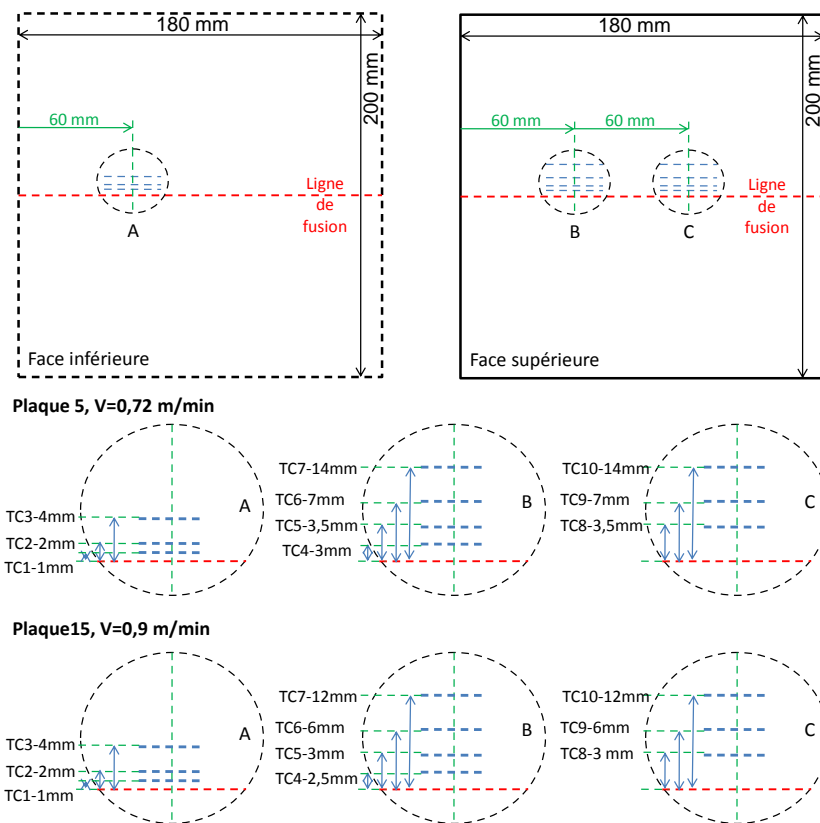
Position des thermocouples sur la plaque 5 soudée à 0,72 m/min ainsi que la plaque 1 soudée à 0,9 m/min
